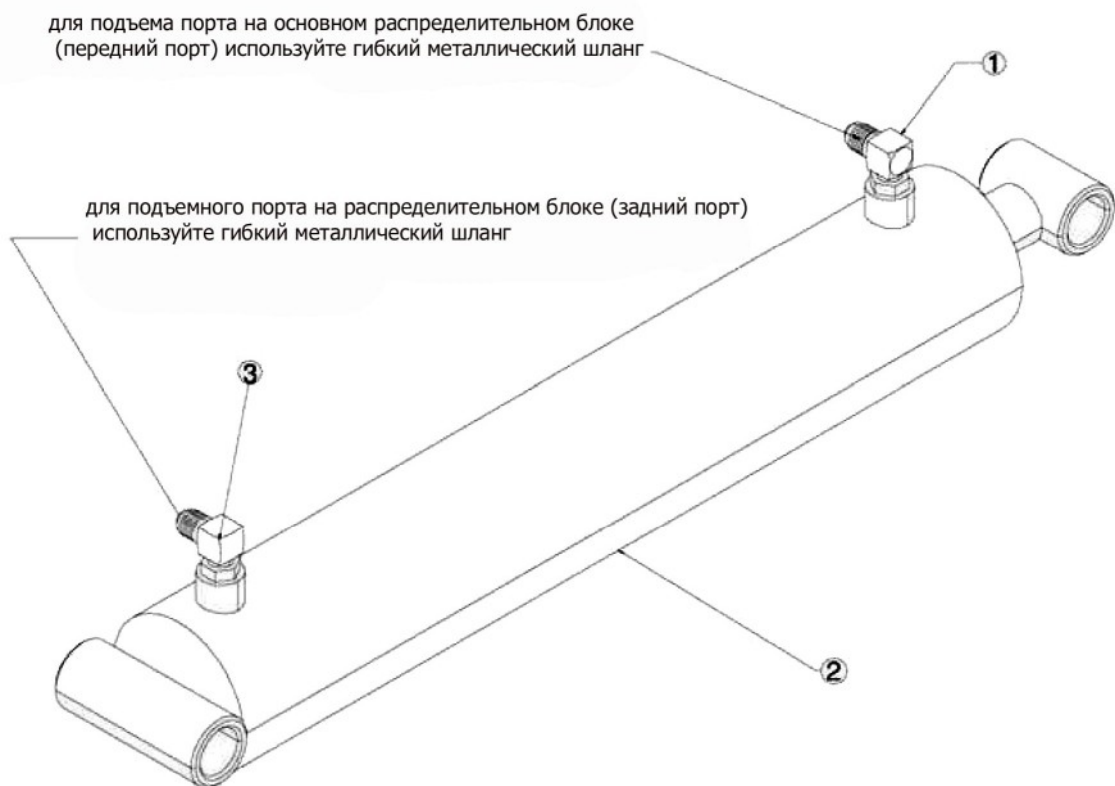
Чертеж гидроцилиндра подъема захвата в сборе - А7013-00
